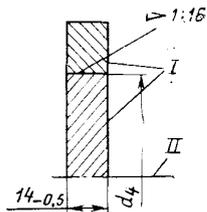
Гладкий калибр-кольцо Г-У для контроля уплотнительного пояска труб ОТТГ, ТБО и его припасовка по гладкой пробке К-Г-Г-У:
